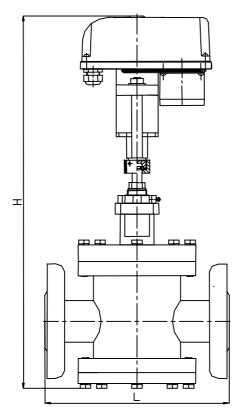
Габаритные установочные и присоединительные размеры клапана.
